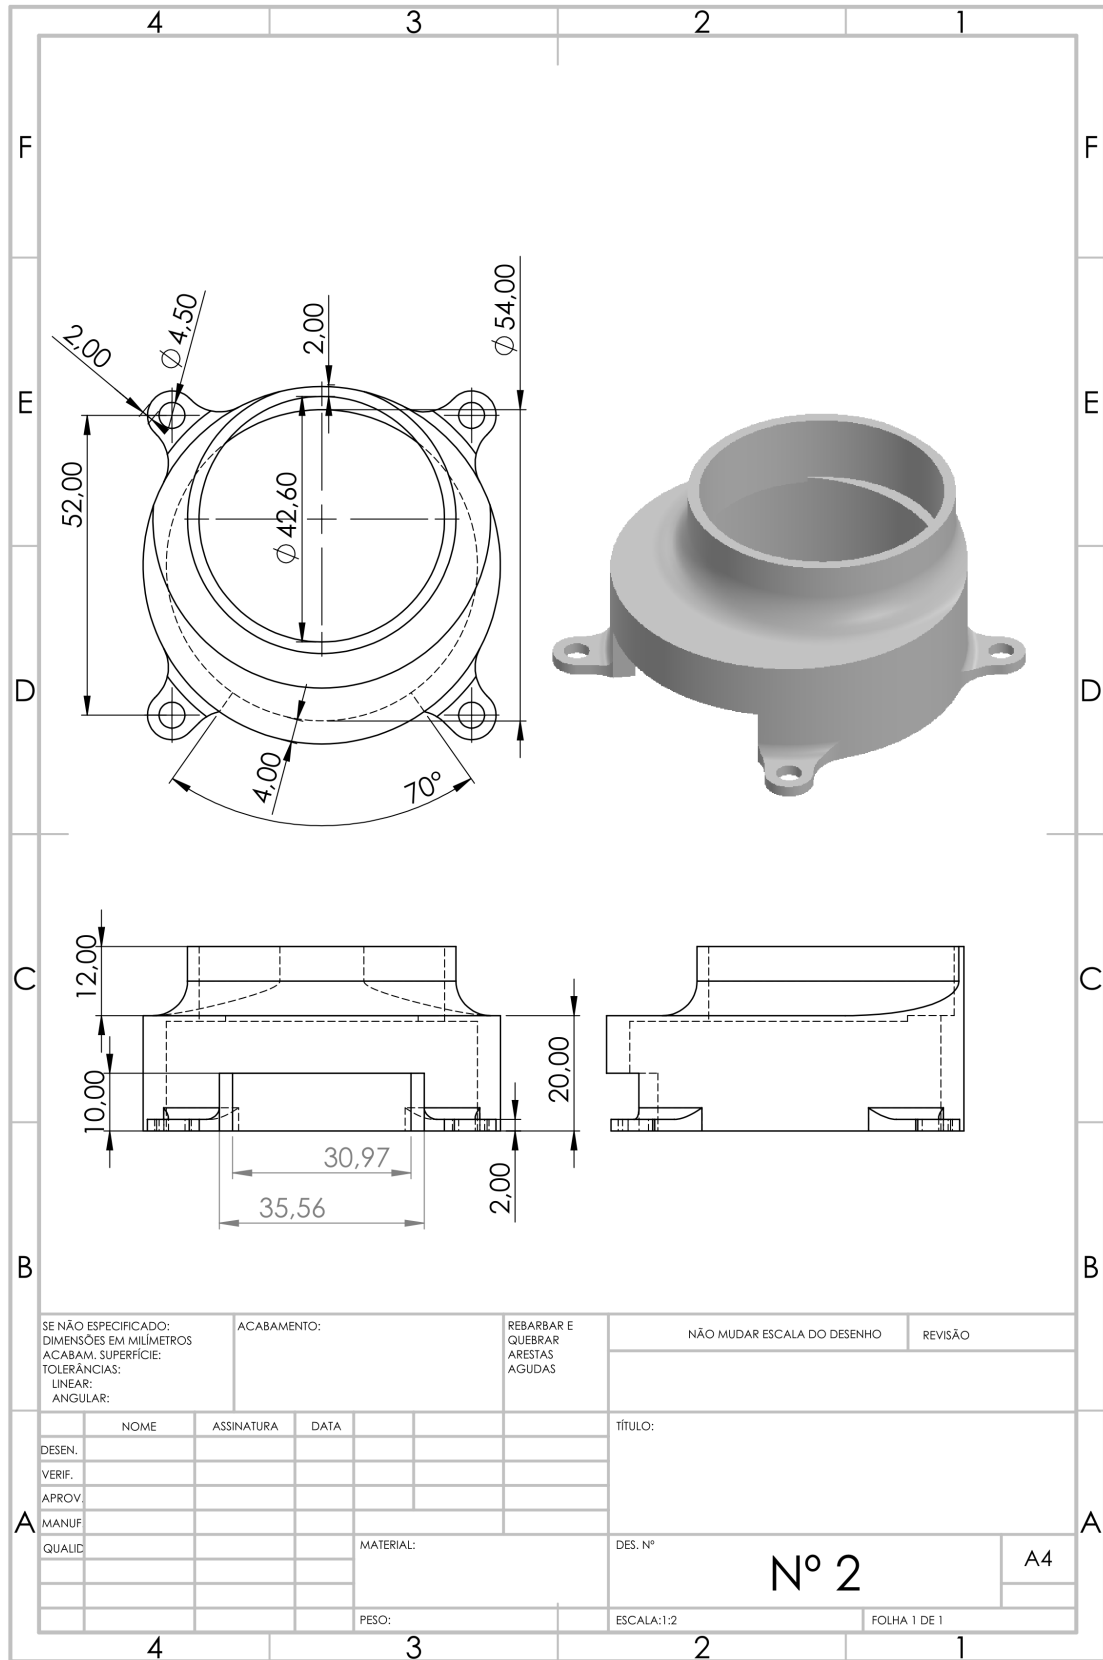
Desenho Técnico do Suporte do Rolamento
